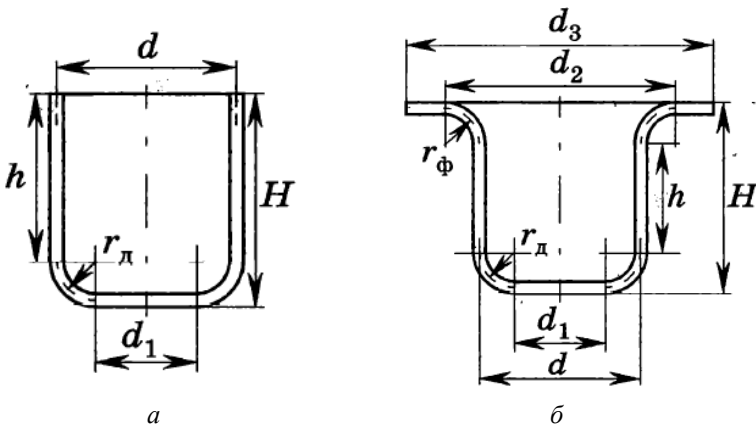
Схемы расчета размеров заготовки для вытяжки:
